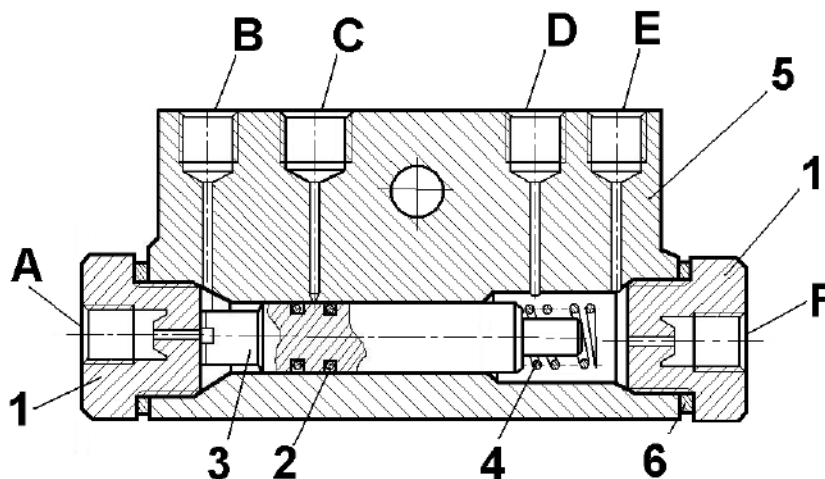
Схема распределителя: 1- пробка; 2- уплотнительное кольцо; 3- поршень; 4- пружина; 5- корпус; 6- шайба; А- выход к регулятору давления (на задний контур); В- вход от главного тормозного цилиндра; С- выход к регулятору давления (байпас); D- отверстие для штуцера прокачки; Е- вход от главного тормозного цилиндра; F- выход на передний контур
